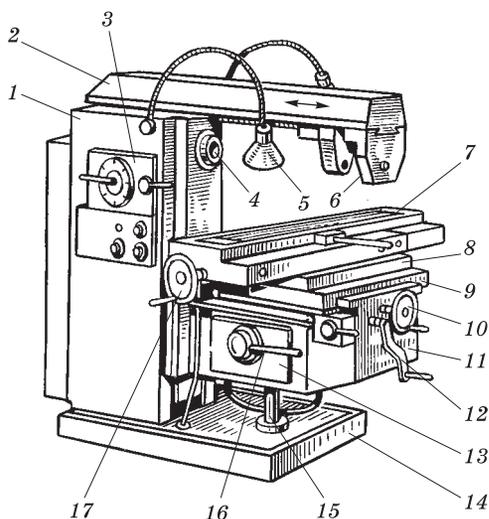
Горизонтально-фрезерный консольный станок:
